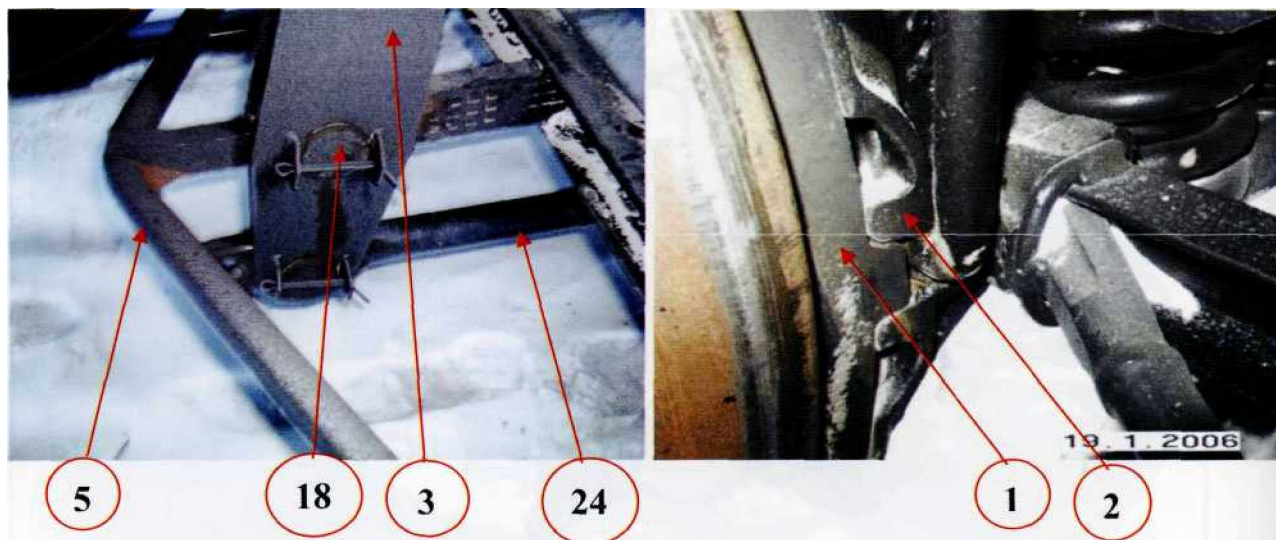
Конструкция тормозной рычажной передачи четырехосного грузового вагона (фрагмент 2)
